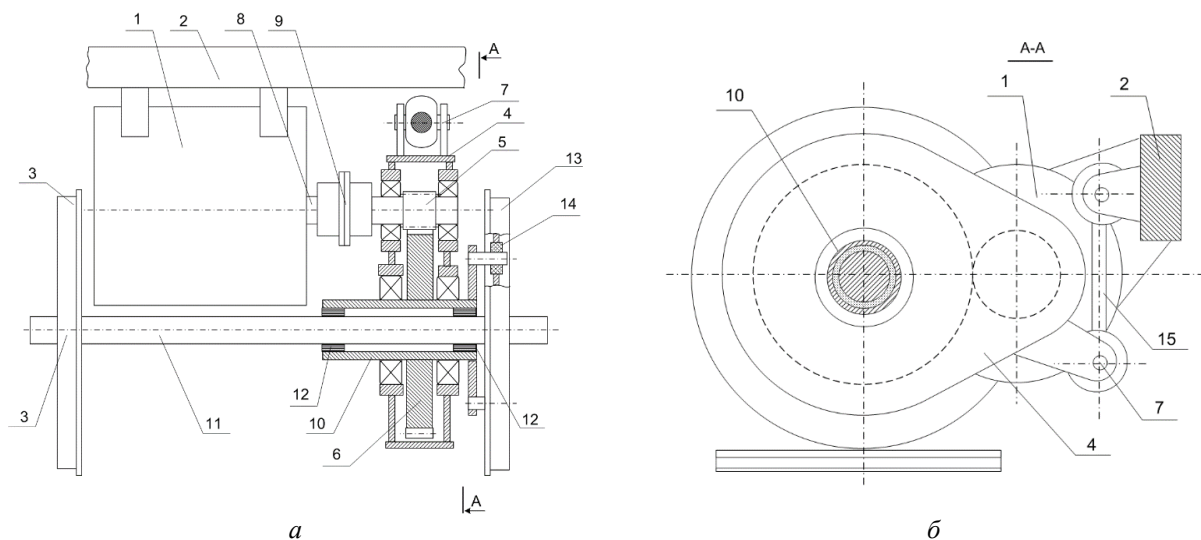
Тяговый привод с опорно-рамным подвешиванием ТЭД и осевым редуктором с размещением упругих элементов в колесном центре: а – общий вид; б – вид со стороны осевого редуктора; 1 – ТЭД; 2 – рама тележки; 3 – колесная пара; 4 – осевой редуктор; 5 – шестерня; 6 – большое зубчатое колесо; 7 – узел подвески редуктора; 8 – вал ТЭД; 9 – зубчатая муфта; 10 – полый вал; 11 – ось колесной пары; 12 – тонкослойные резинометаллические элементы; 13 – колесный центр; 14 – упругие элементы; 15 – двухшарнирная тяга
